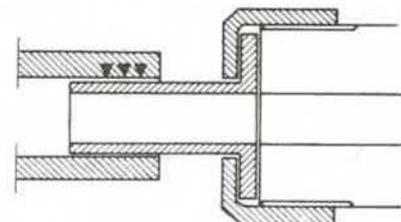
Joints coulissants permettant un déplacement du stator de la pompe.
